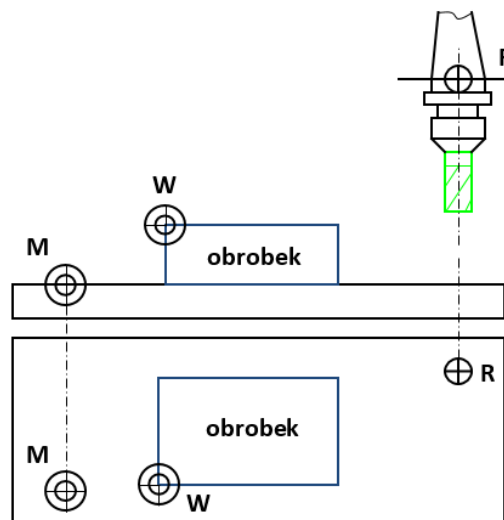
Souřadnicový systém CNC stroje [14]
